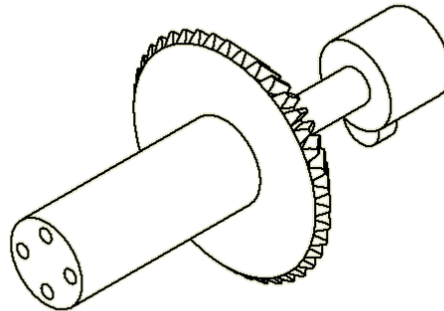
Vista Isométrica del ensamble de acoplamiento de gripper
